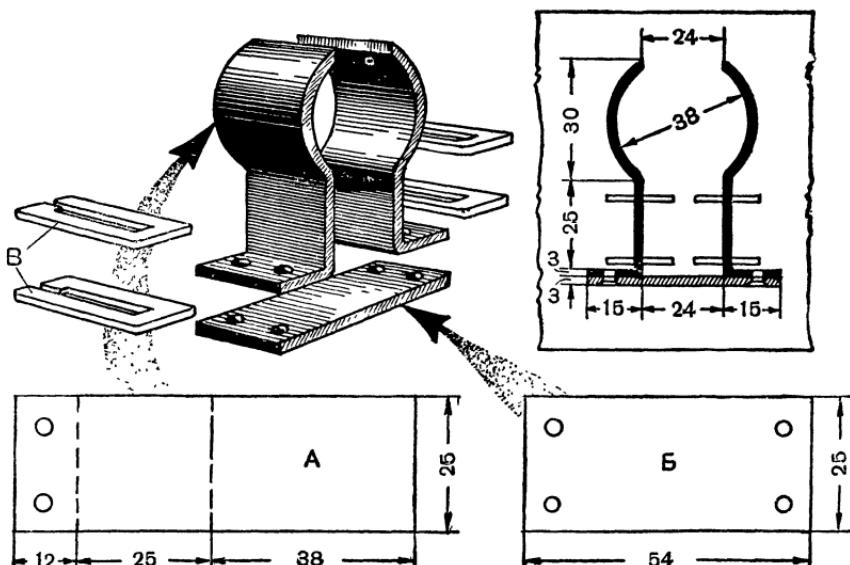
Детали статора № 3 (рис. 14): А — заготовка для башмака; Б — соединительная планка; В — щечки катушки.
